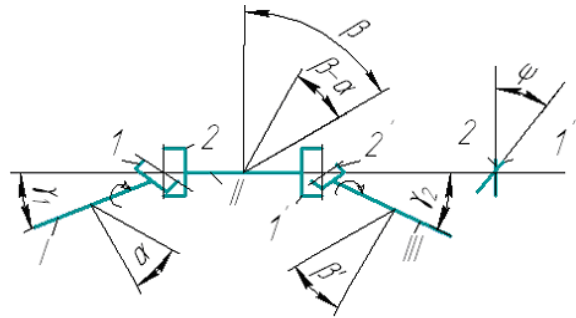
Схема карданной передачи с двумя шарнирами и обозначением углов
